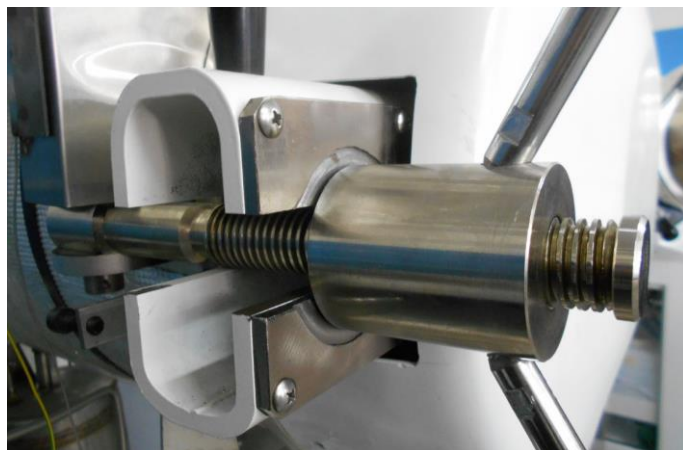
Механизм винтового затвора камеры стерилизатора ГК-100-3
